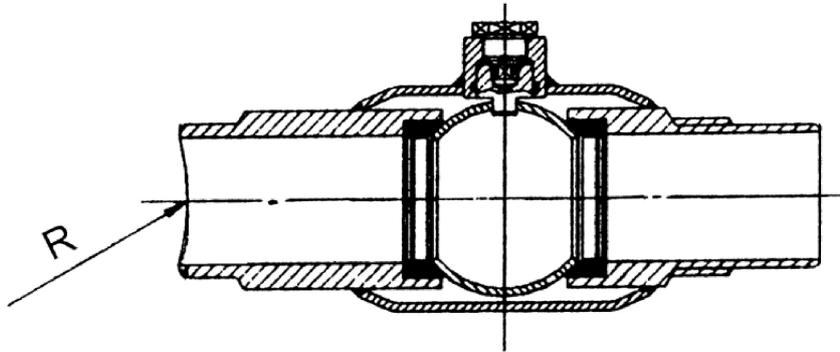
Anpassung der Anschweißendenkontur passend zum Hauptrohr
